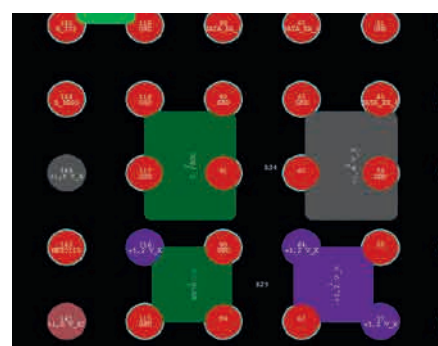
Близкое расположение двухполюсников чревато блокировкой контактов BGA
